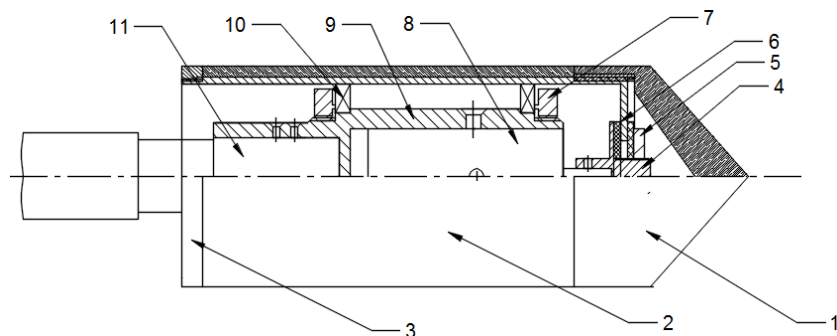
Конструкция экспериментальной модели: 1 – сменная головная часть; 2 – корпус модели; 3 – гайка для крепления донного стабилизатора; 4 – муфта; 5 – гайка; 6 – шайба; 7 – стопорная гайка подшипника; 8 – электродвигатель; 9 – переходной стакан; 10 – подшипник качения; 11 – поршень тензовесов
